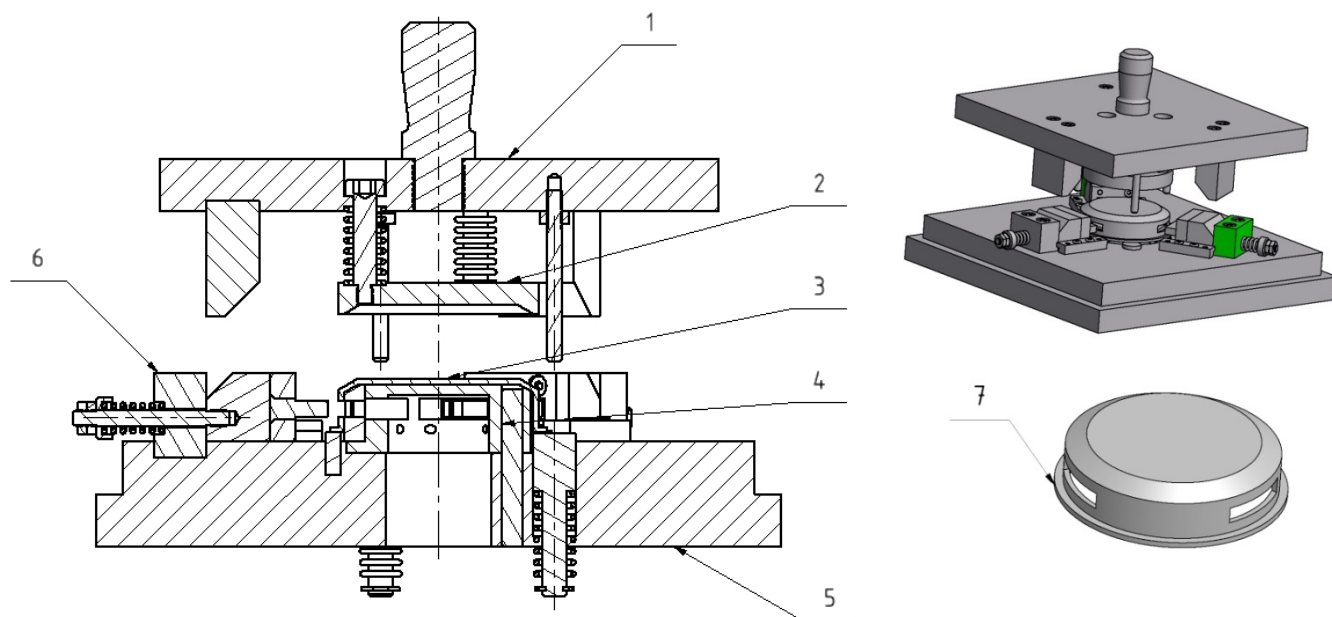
Lochwerkzeug mit Keilschieber für Deckel
